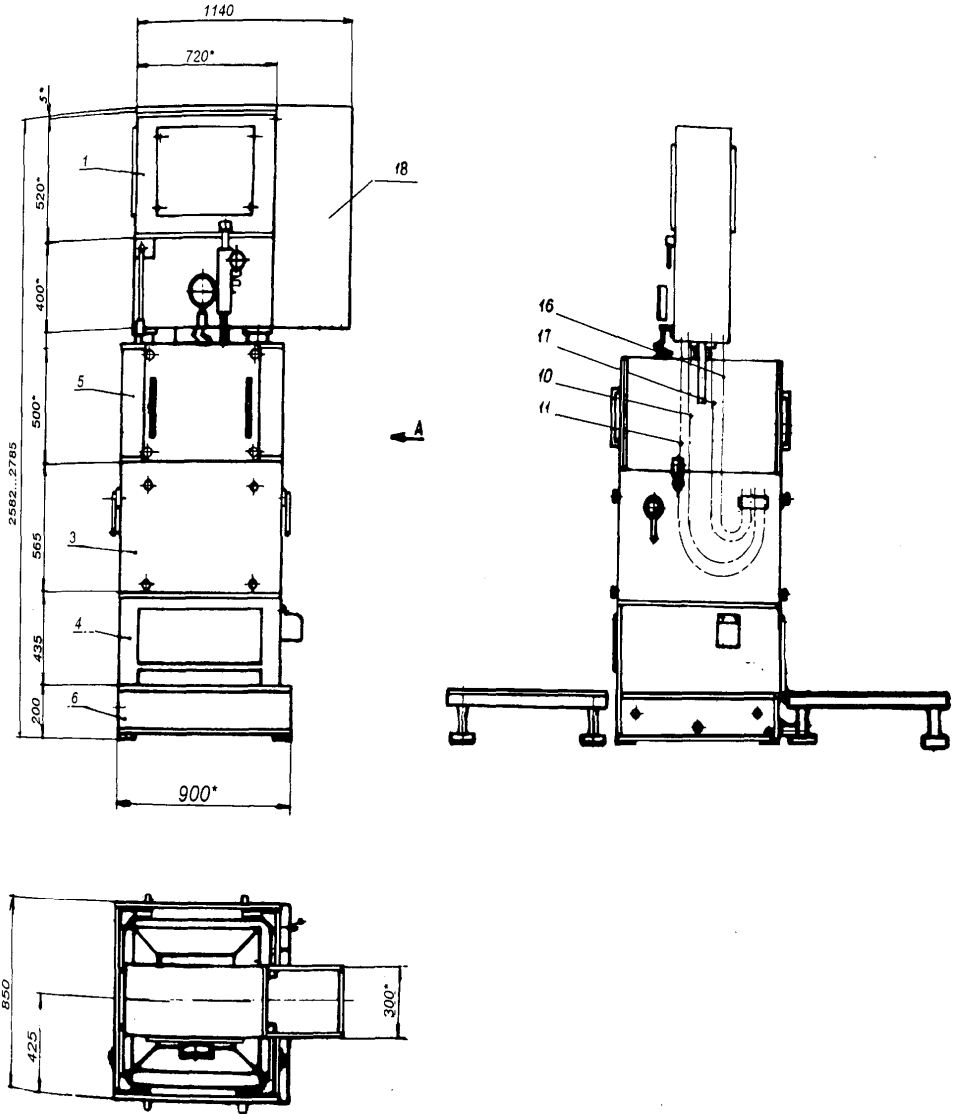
Загальний вид верстату «Дуга – 8Д»
